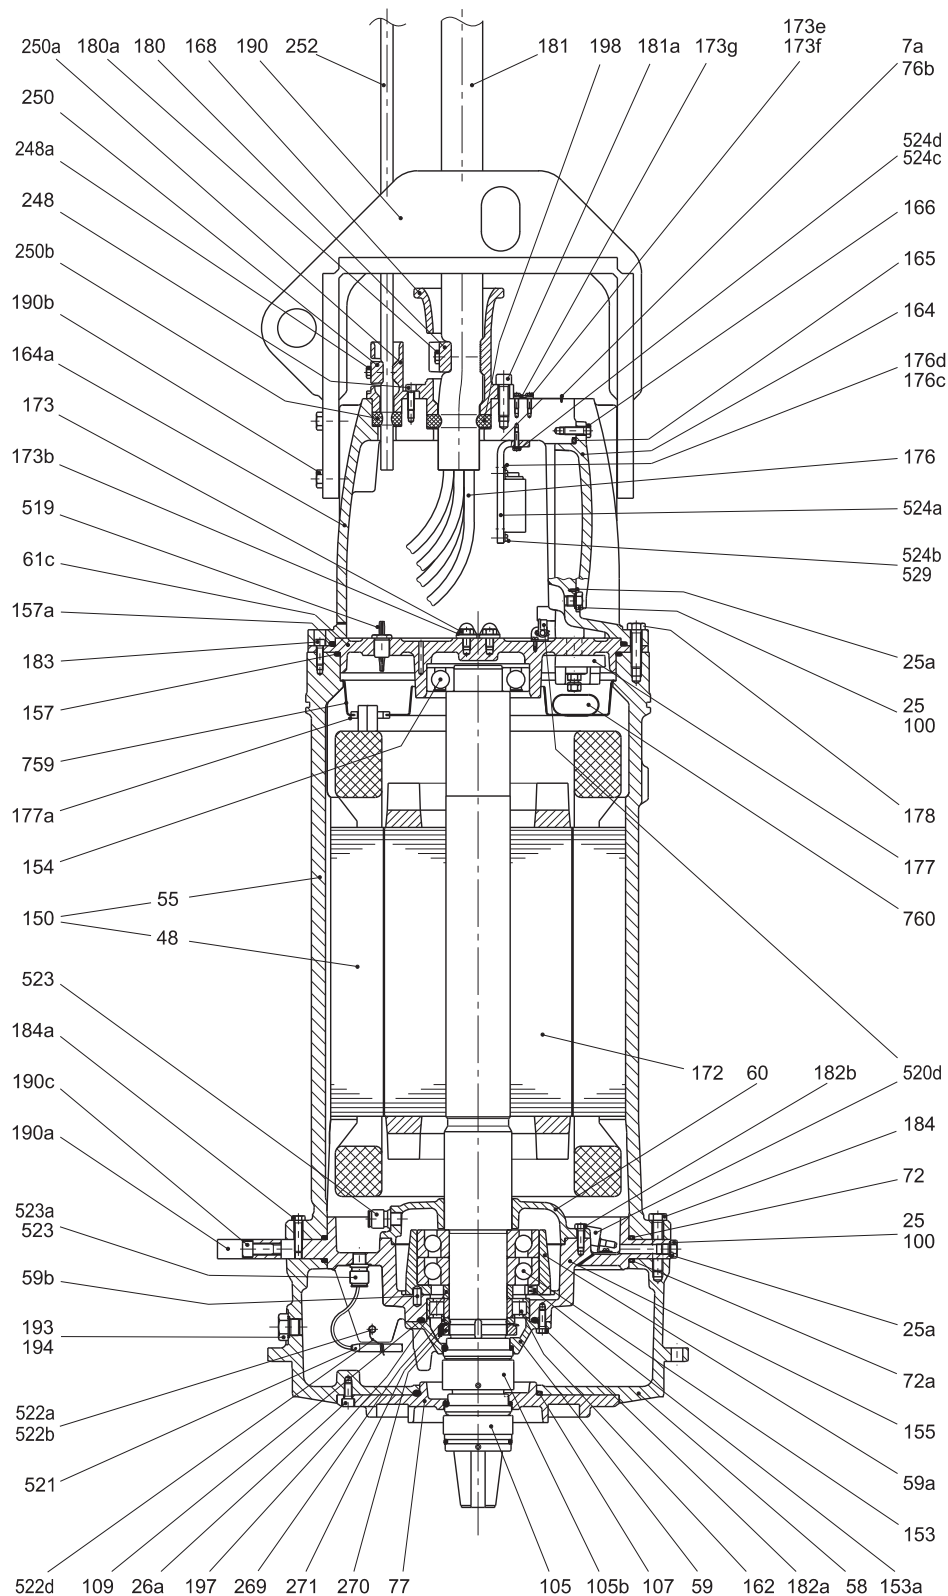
Типоразмер 72, двигатель без охлаждающего кожуха.
